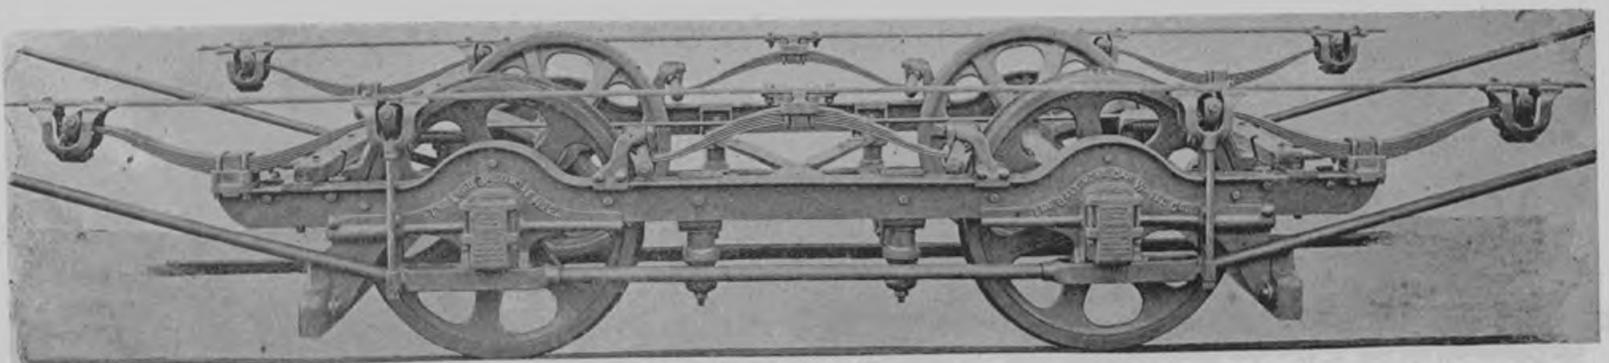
CHASSIS LÉGER DE LA BALTIMORE WHEEL C°
